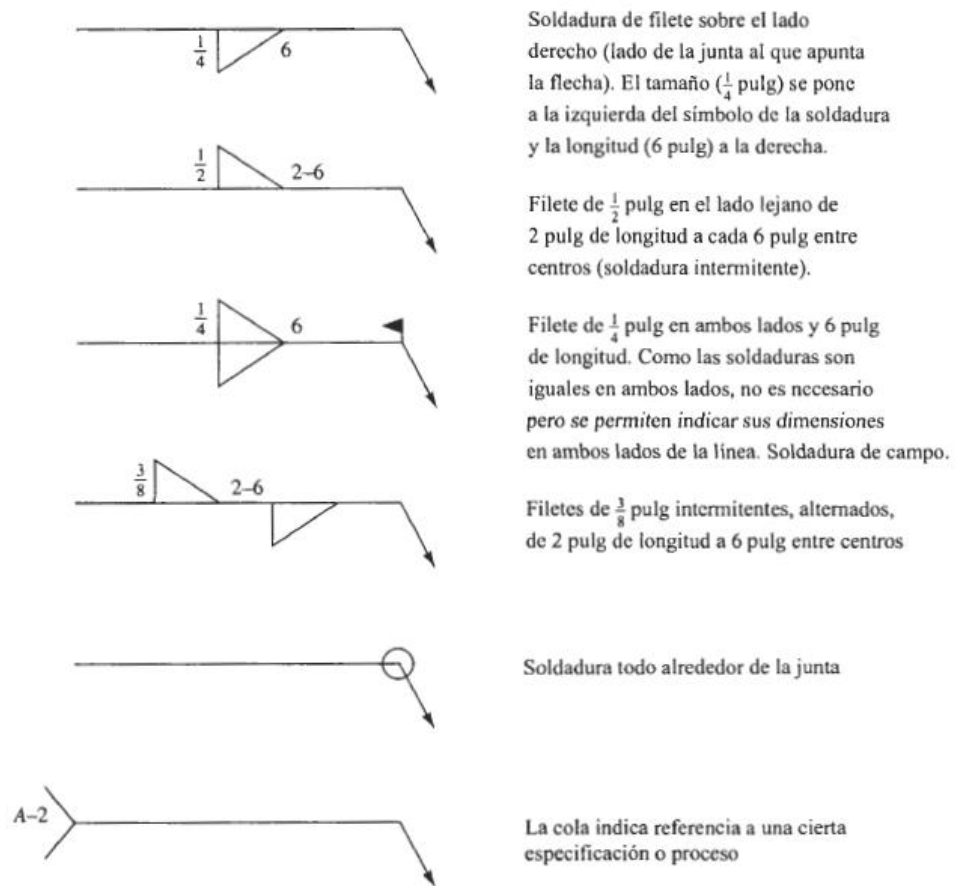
ejemplos de símbolos de soldadura
